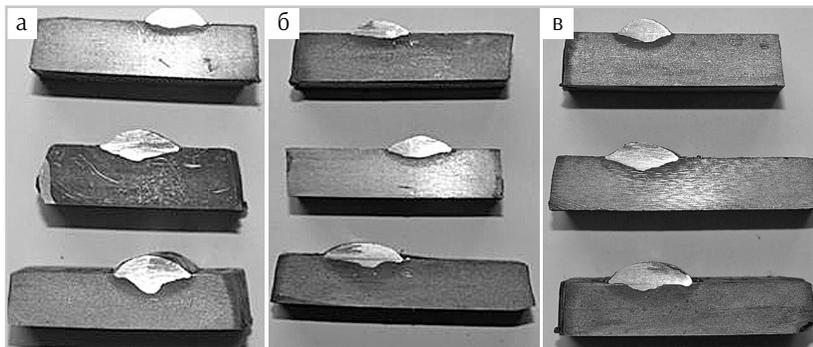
Макрошлифы образцов с наплавкой, выполненные механизированной сваркой в смеси газов Ar + CO₂ (82% + 18%): а – Св-08Х20Н9Г7Т; б – Thermanit X (УТР А63); в – ОК Autrod 16.95.
